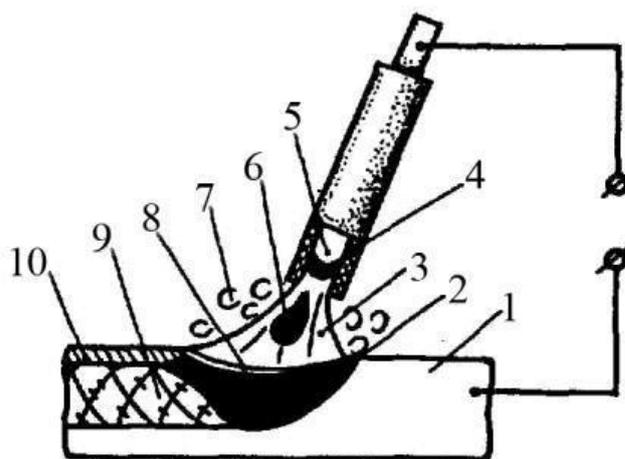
Схема процесса ручной дуговой сварки с покрытыми электродами
